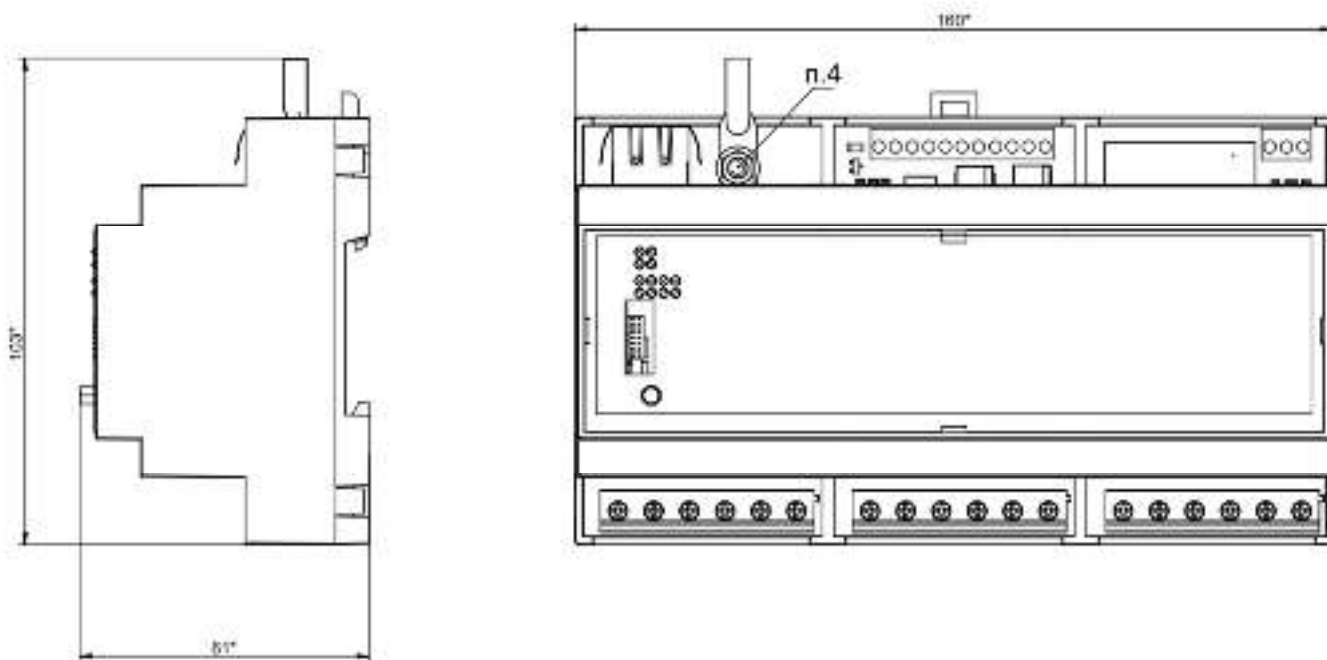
Внешний вид и габариты прибора Пассер-Т
